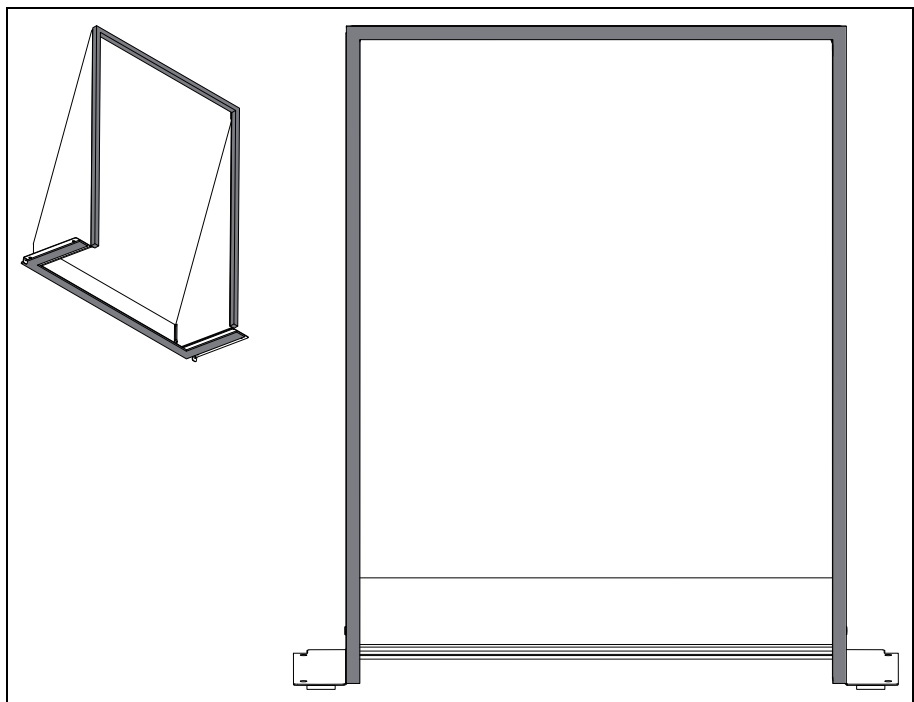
Dichtung an Anlagefläche Vertikalteil zu Rücktür
